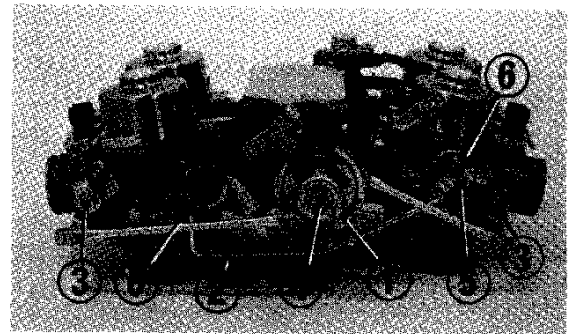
(1) Umlenkhebel (4) Bolzen
